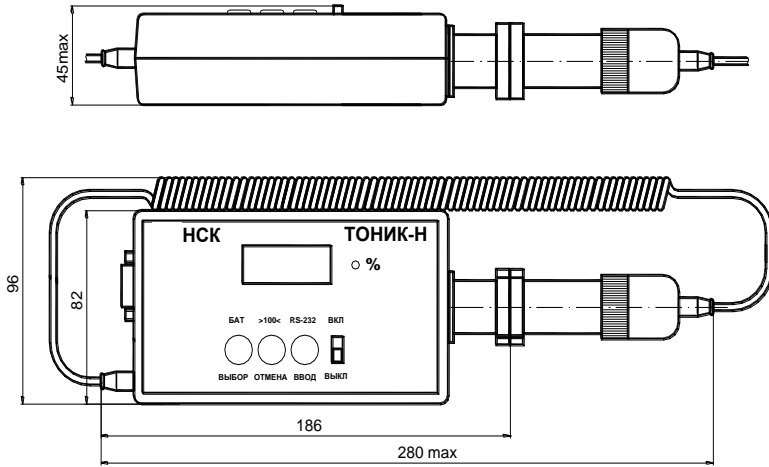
Габаритный чертеж прибора в рабочем положении
